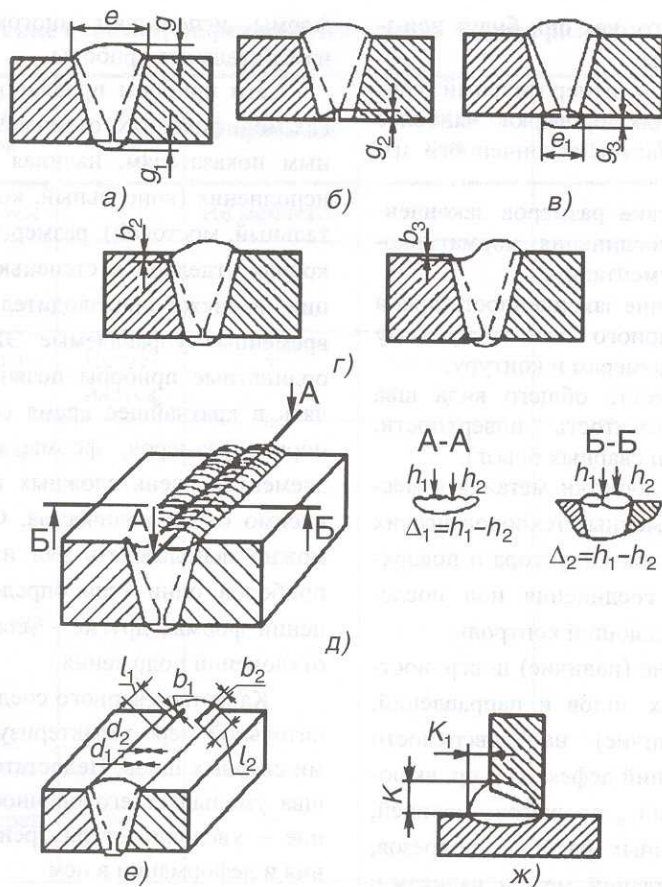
Размеры сварного шва и его дефектов, подлежащие измерительному контролю: a – ширина (e), выпуклость (g, g_1); b – вогнутость корня сварного шва (g_2); $в$ – ширина лицевой стороны двухстороннего сварного шва (e_1), выпуклость (g_3); $г$ – подрез зоны сплавления (b_2) и неполное заполнение разделки кромок (b_3); $д$ – чешуйчатость (Δ_1) и западание между валиками шва (Δ_2); $е$ – размеры поверхностных дефектов; $ж$ – катет шва (K, K_1)
